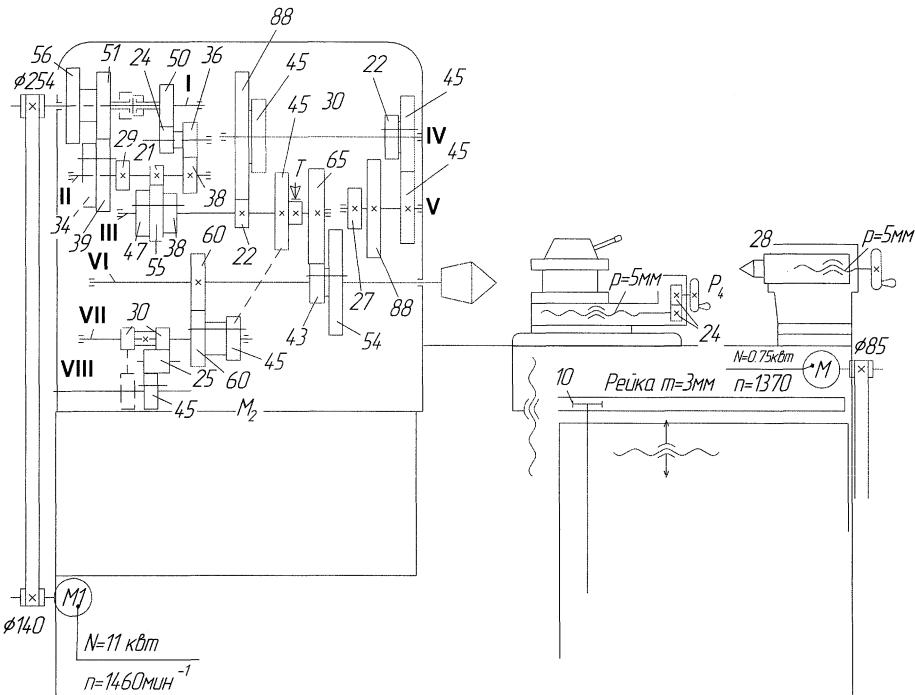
Кинематическая схема коробки скоростей станка 1К625
